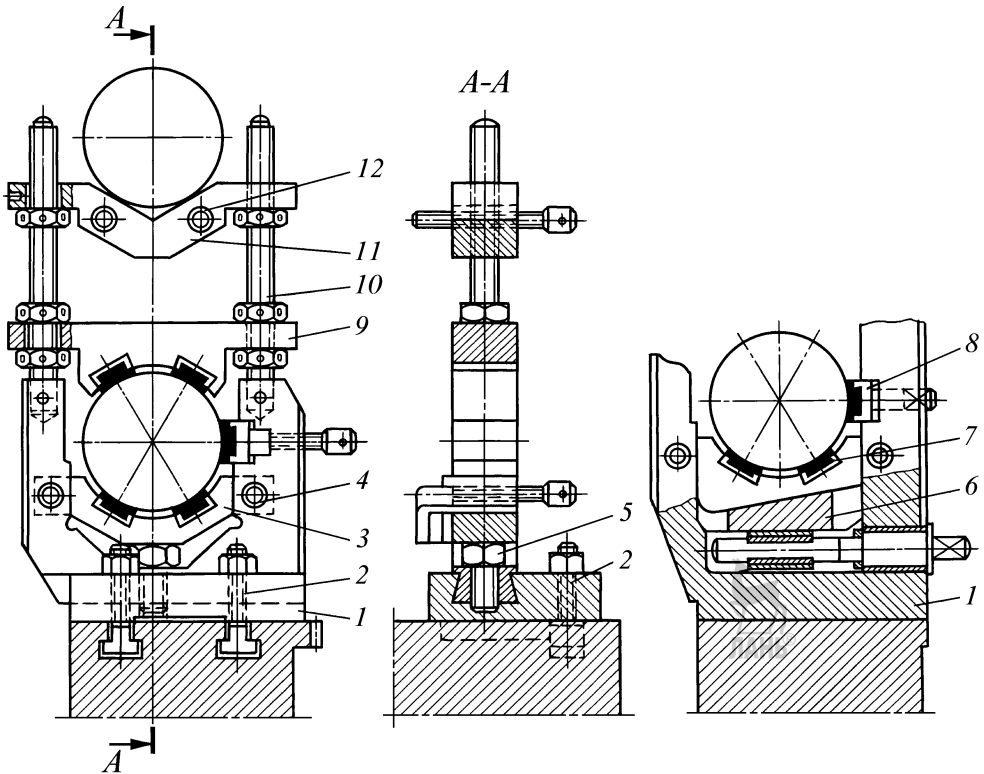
Двойной люнет калибровочного вальцетокарного станка:
